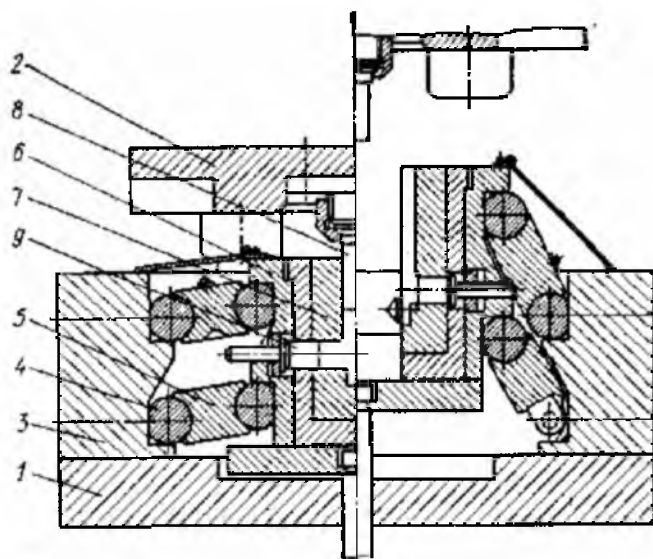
Ковочный пакет с вертикальным разъемом матриц
